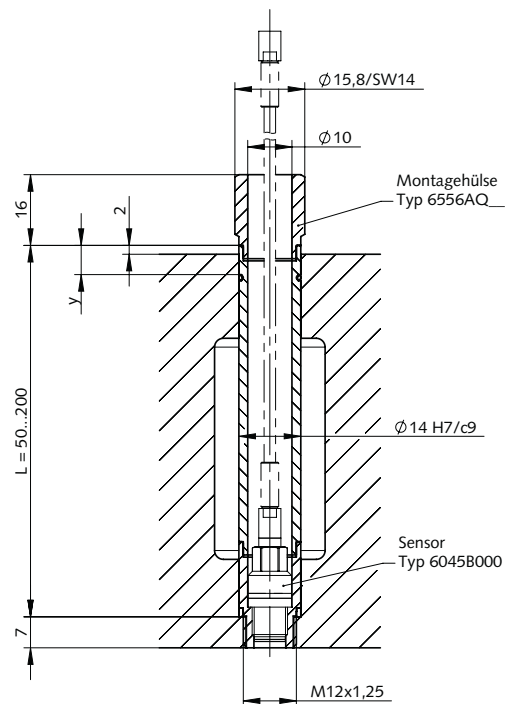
Einbau mit Montagehülse Typ 6556AQ...
